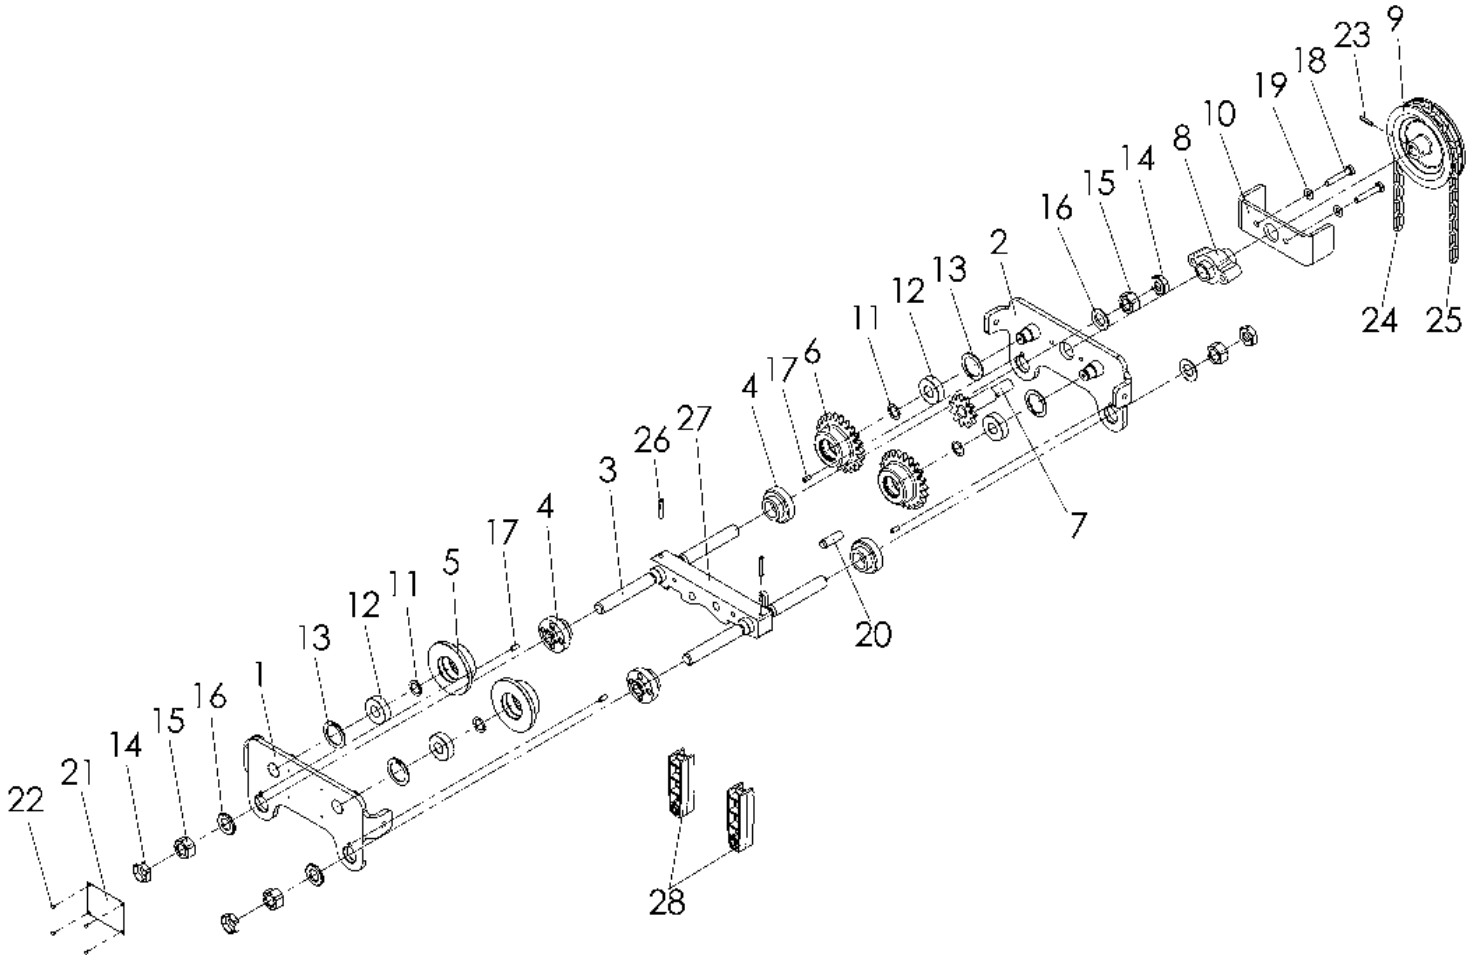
CARRO DE EMPUJE Y DE ENGRANAJES DE 3 - 5 TONELADAS
